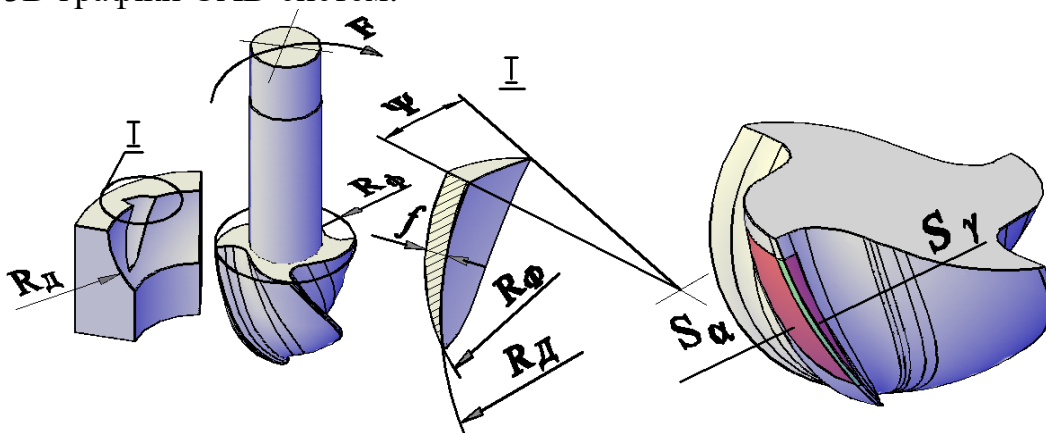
Формування перетину зрізу заготовки R_d товщиною f фрезою R_ϕ
